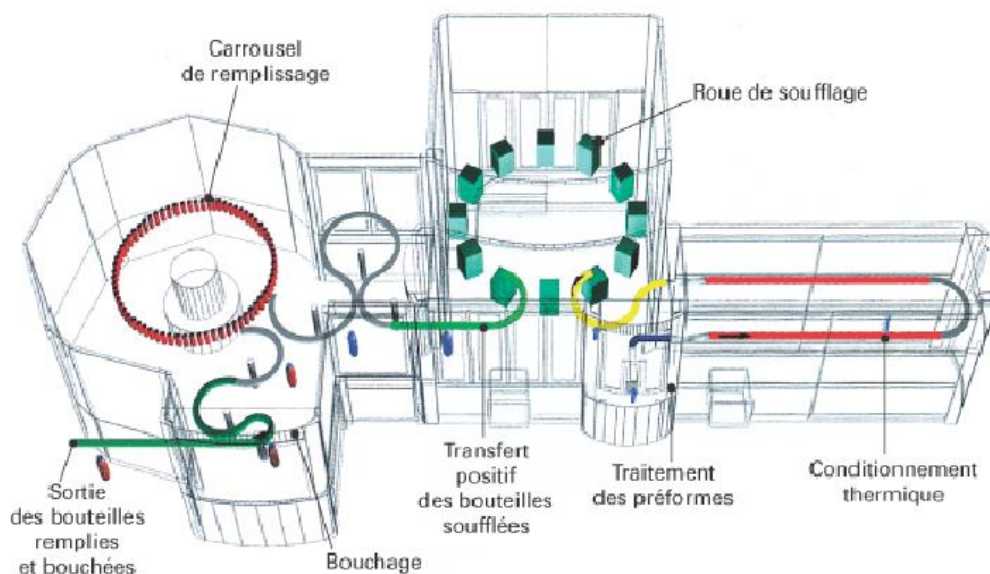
Machine de soufflage des bouteilles en PET, remplissage et bouchage
